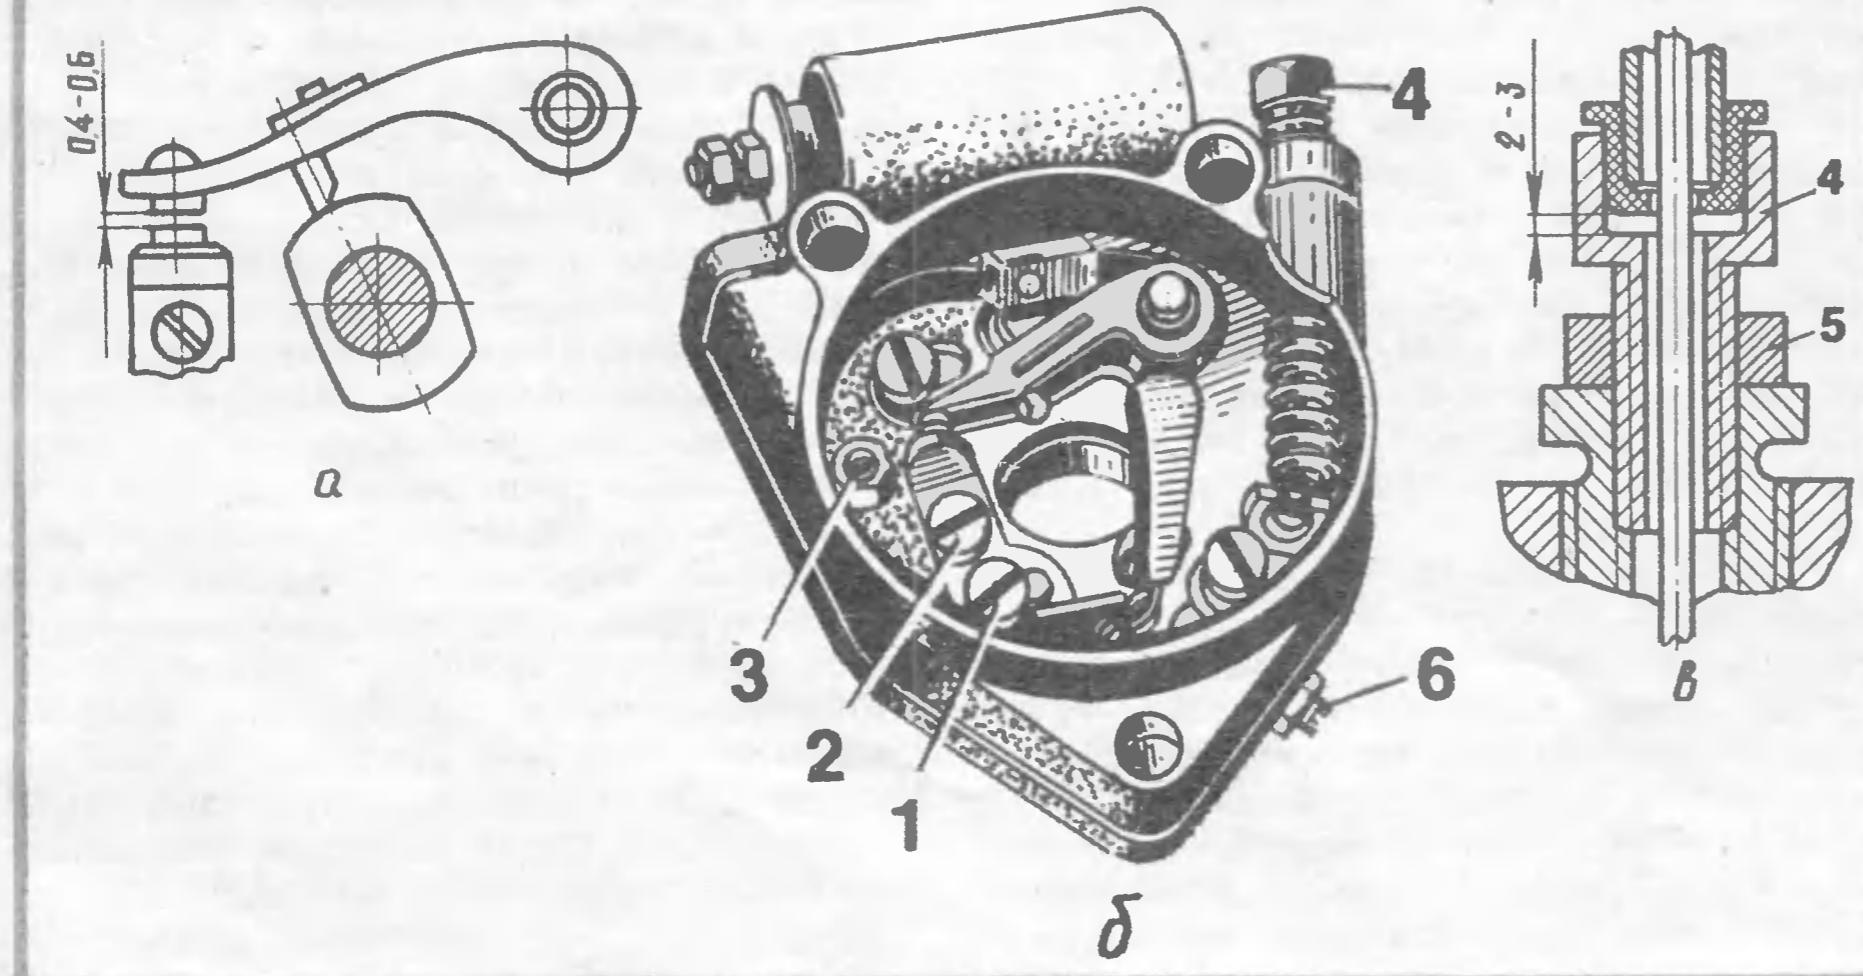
Прерыватель с автоматом опережения зажигания ПМ302-А: а — общий вид; б — вид спереди (грузики условно раздвинуты); 1 — стопорный винт; 2 —
